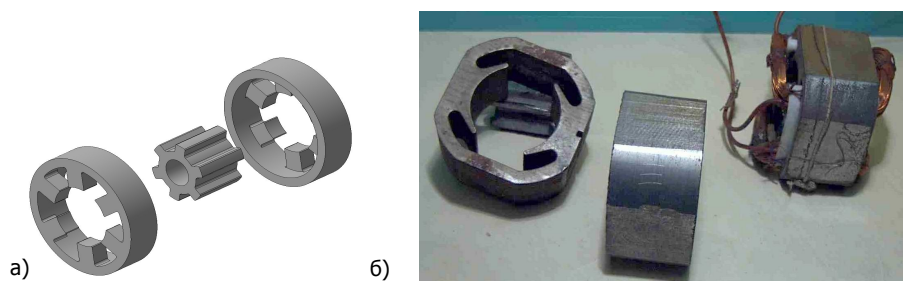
D-дизайн конструкции элементов (ротор-статор) электродвигателя (а) и внешний вид прессованного «статора» из порошковой композиции конструкции ДГТУ-РГУПС – ИПМНАУ г.Киев взамен пакетированного (б)
